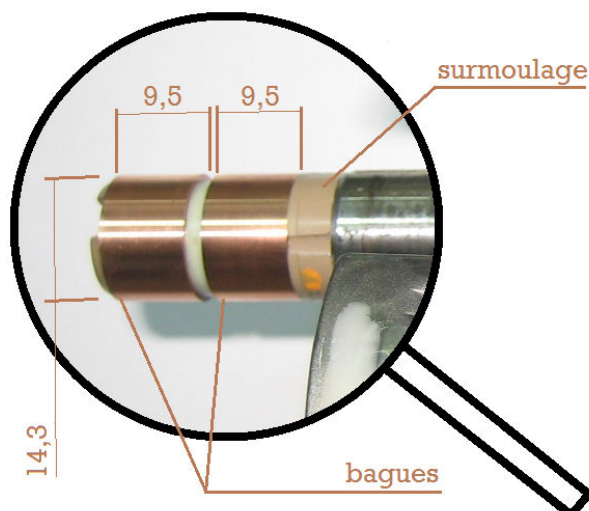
Zoom sur les bagues en partie arrière du rotor et dimensions de celles-ci.
